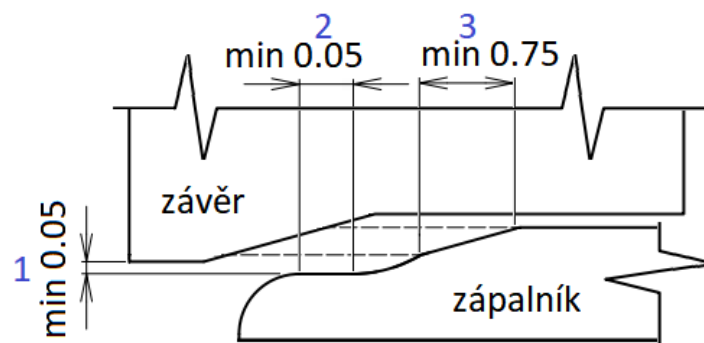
Případy geometrií pro ukázkou geometrických omezení
